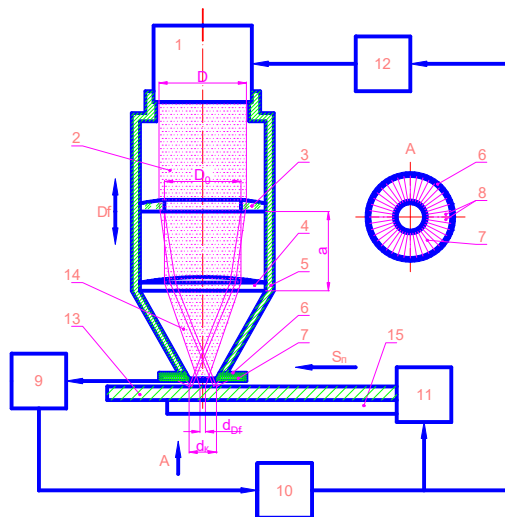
Схема пристрою для лазерної обробки поверхонь зі стабілізацією рівня поглинання енергії проміння: 1 – випромінювач; 2 – лазерний пучок; 3 – лінза з отвором; 4 – лінза фокусувальна; 5 – корпус; 6 – корпус датчика; 7 – датчик; 8 – сектори датчика; 9 – вимірювач; 10 – процесор; 11 – механізм переміщення; 12 – блок живлення випромінювача; 13 – заготовка; 14 – сконцентрований пучок; 15 – стіл технологічний
